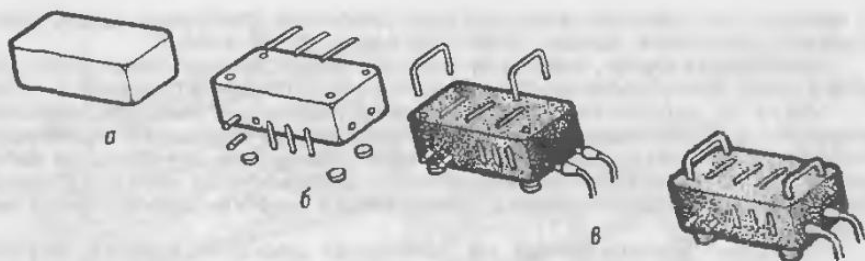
Изготовление пультов: а - корпус; б - выступающие детали; в - пульт в сборе
